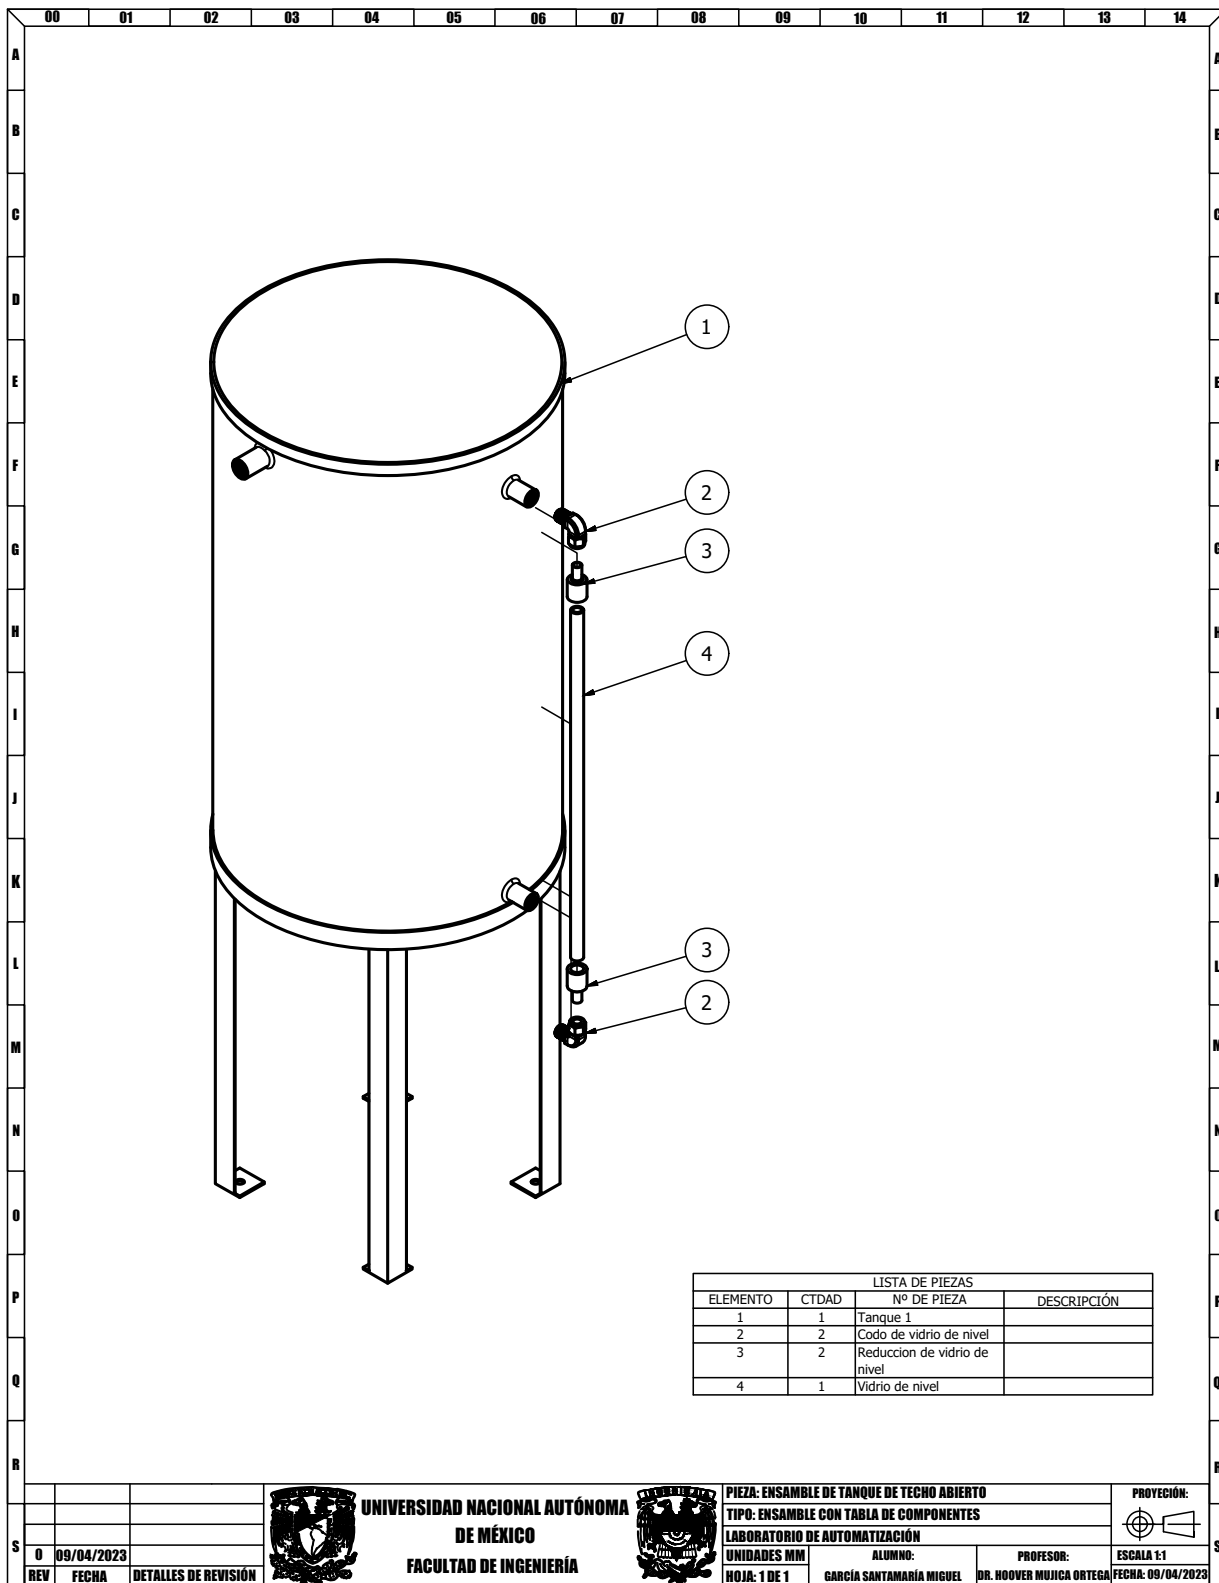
Ensamble explosionado y tabla de componentes de tanque de techo abierto
